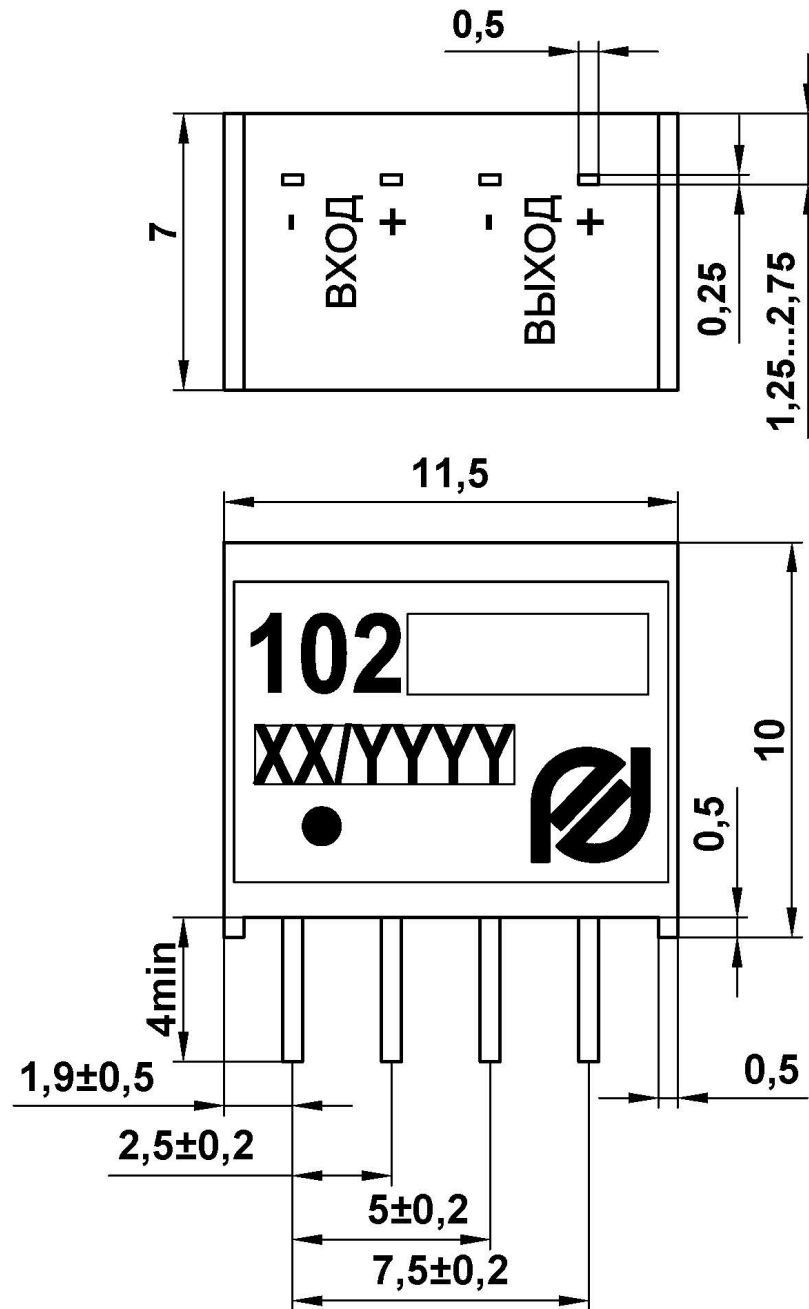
Габаритный чертеж одноканальных модулей в конструктиве «Е», корпусного исполнения
